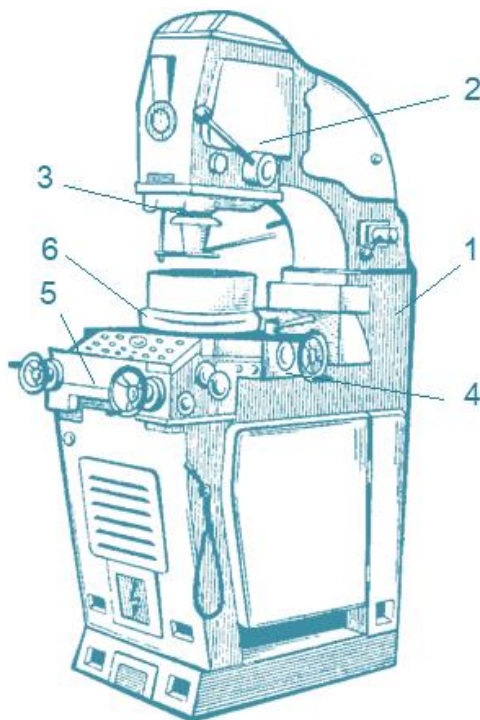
Зовнішній вигляд ультразвукового верстата: 1 – станина; 2 – головка ультразвукова; 3 – механізм робочої подачі; 4 – поздовжній стіл; 5 – поперечний стіл; 6 – поворотний круглий стіл
